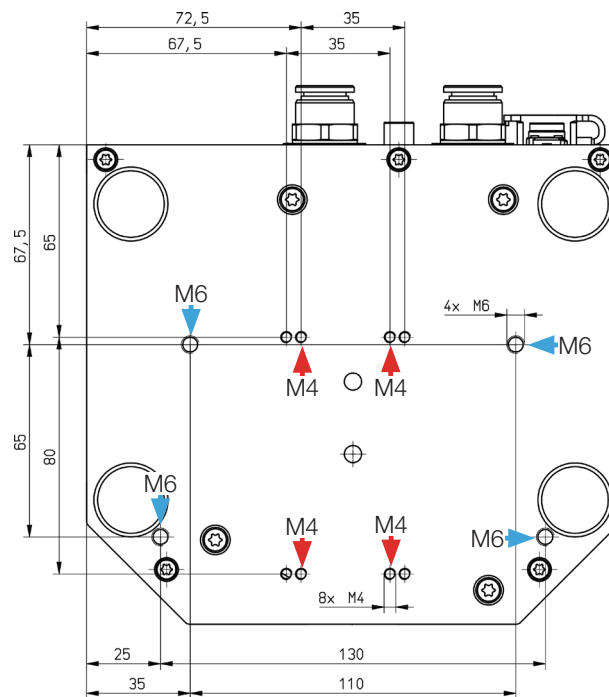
Befestigungsgewinde M4 und M6 im Boden des Gehäuses am CPM+ F-10 (Maße in mm)
